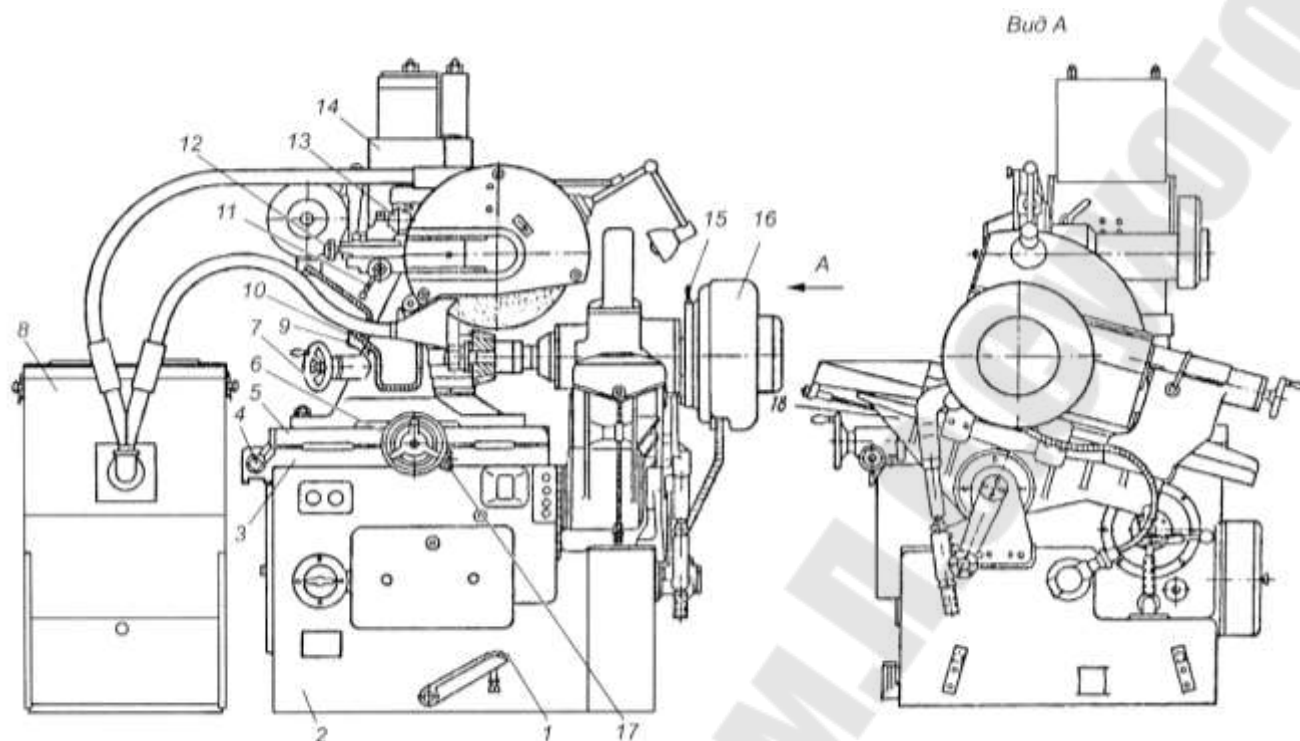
Общий вид зубошлифовального полуавтомата модели 5893: 1 – панель тормоза; 2 – станина; 3 – нижний стол; 4 – квадрат продольного перемещения абразивного инструмента; 5 – верхний стол; 6 – маховичок поперечного перемещения инструмента; 7 – маховичок вертикального перемещения инструмента; 8 – пылесос; 9 – колонна; 10 – поворот колонны; 11 – рукоятка продольного перемещения приспособления для правки абразивного инструмента; 12 – кнопка для установочного перемещения приспособления; 13 – поворотная кнопка для поперечного перемещения приспособления; 14 – шлифовальная бабка; 15 – рукоятка ручного поворота рабочей головки; 16 – рабочая головка; 17 – маховичок тонкой поперечной подачи абразивного инструмента; 18 – салазки
